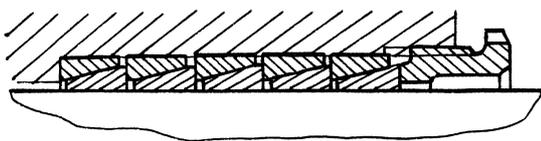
Сальник с металлическими пружинно-затяжными кольцами
